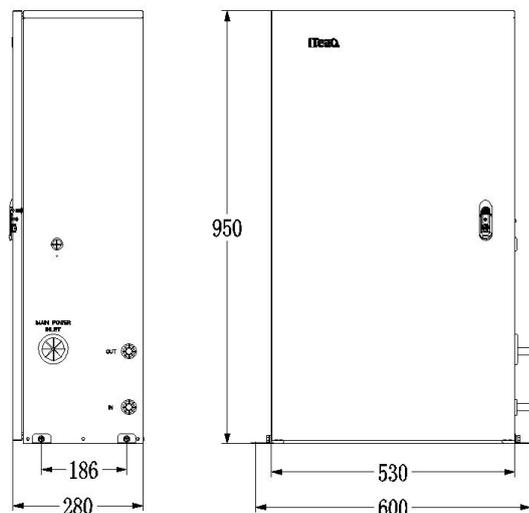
Габаритные размеры энергосберегающего модуля фторопластового насоса
